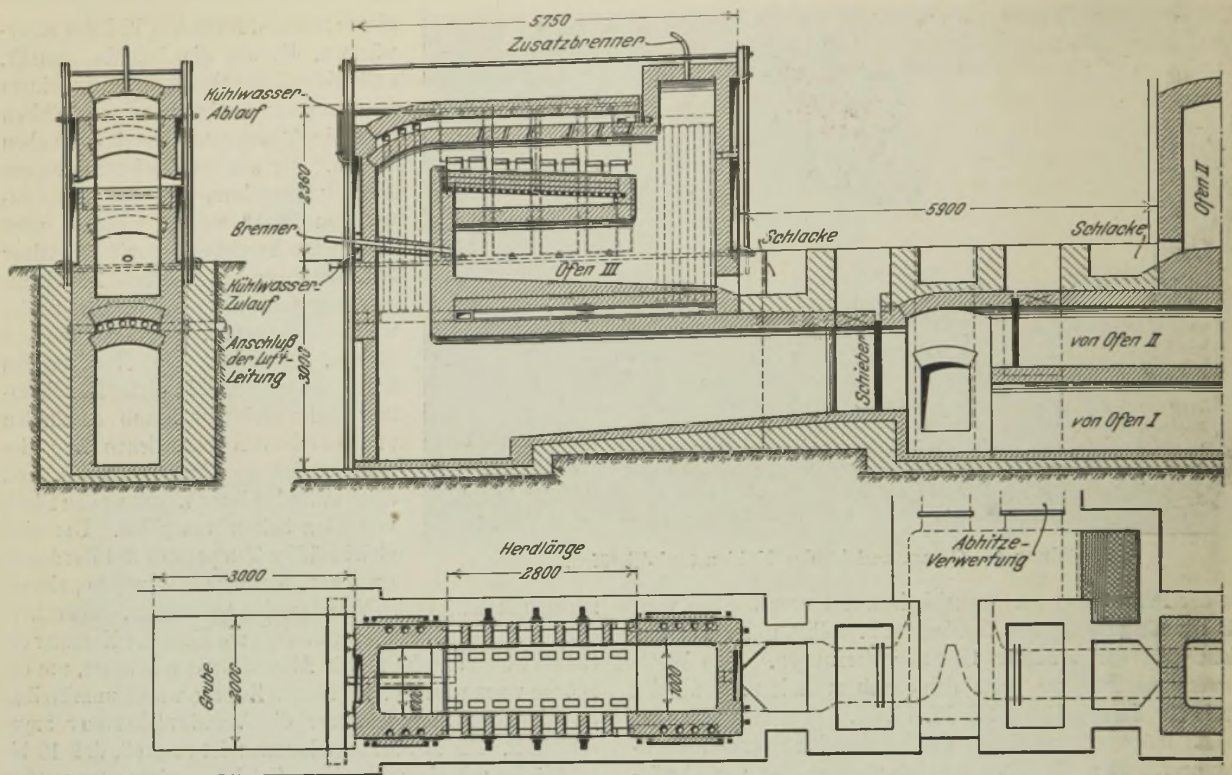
Schweißofen III mit Kohlenstaubfeuerung.
